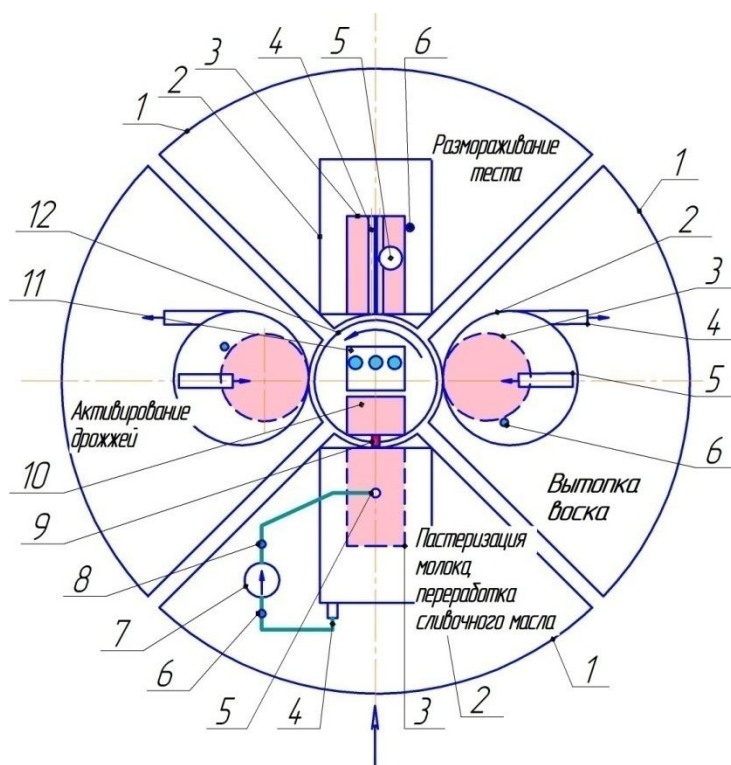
Схема СВЧ-агрегата для переработки продукции: 1 – передвижной корпус; 2 – цилиндрический экранный корпус СВЧ; 3 – резонаторная камера; 4 – выгрузной патрубков; 5 – измельчающий и загружающий механизм; 6 – датчики контроля процесса; 7 – перекачивающий насос; 8 – счетчики жидкости; 9 – излучатель; 10 – генераторный блок; 11 – контрольно-измерительный блок; 12 – экранный корпус для генераторного блока
